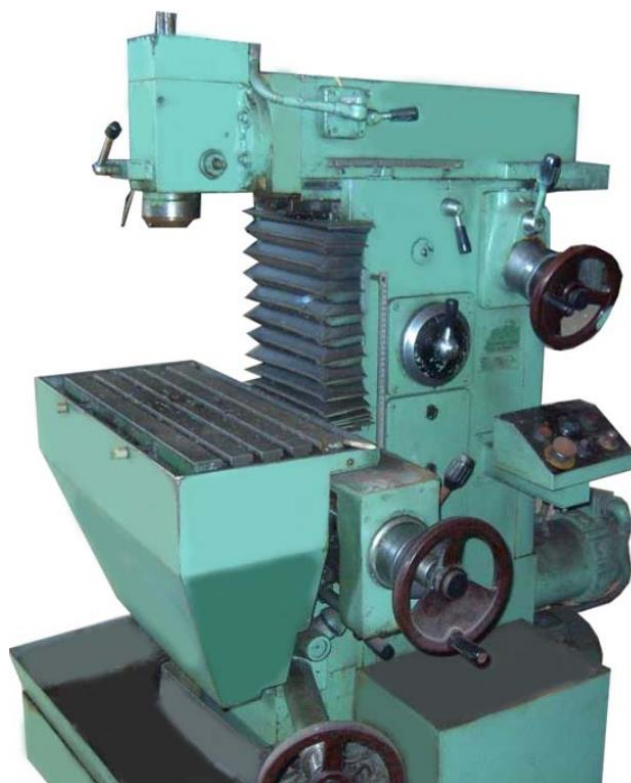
Загальний вигляд верстату BM130 [5]
